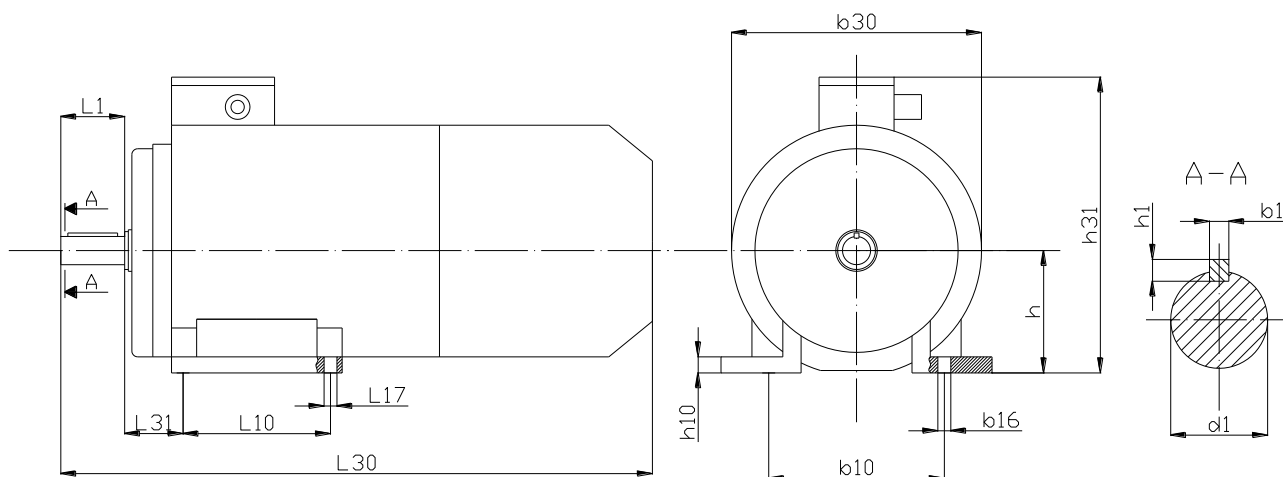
Габаритные и установочно-присоединительные размеры
